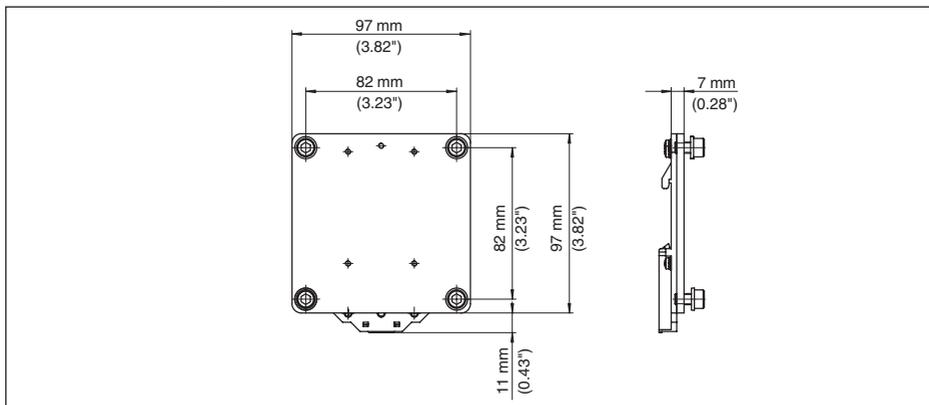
Placa adaptadora para montaje en regletas de montaje del VEGADIS 81
